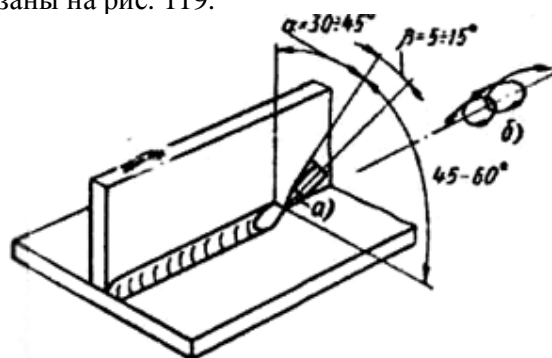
Положение (а) и траектория (б) горелки при полуавтоматической дуговой сварке в углекислом газе
